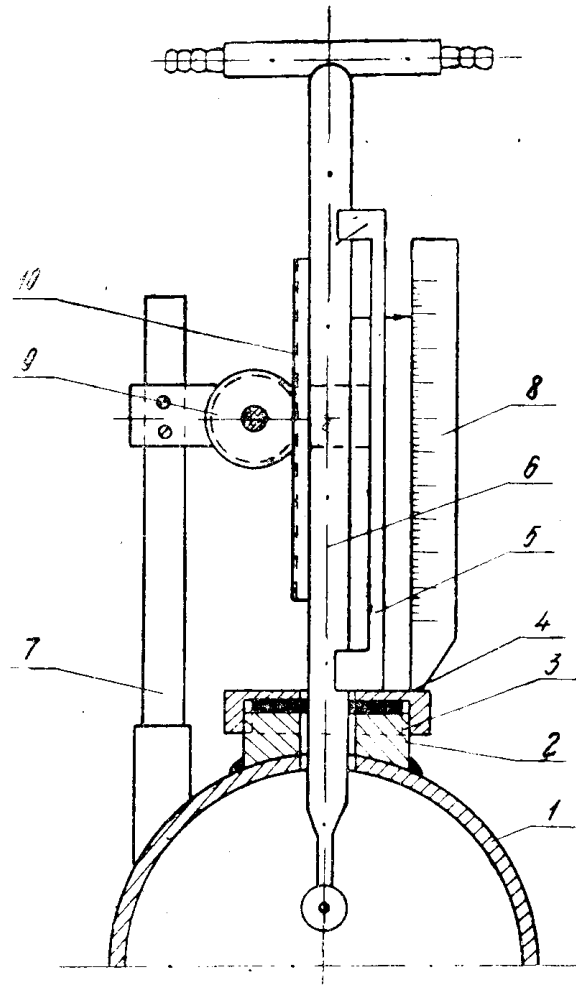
Приспособление для снятия эпюры скоростей: 1—труба; 2—штуцер; 3—гайка; 4—резиновый уплотнитель; 5—направляющая стойка; 6—пневмометрическая трубка; 7—стойка; 8—шкала; 9—зубчатое колесо; 10—зубчатая рейка.
